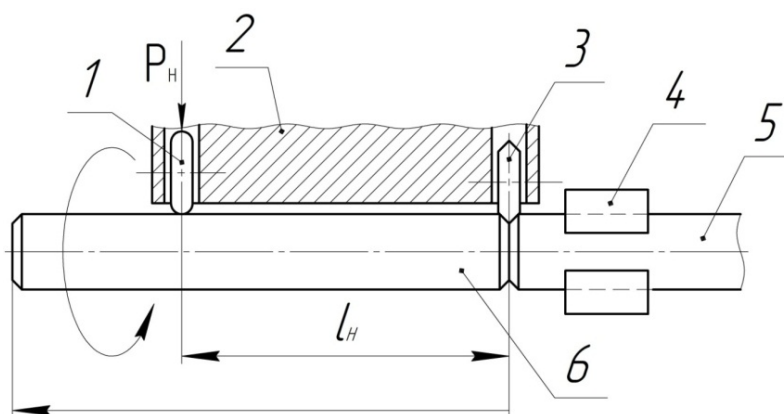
Схема разрезки прутка на длинномерные заготовки: 1 – нажимной ролик; 2 – ротор; 3 – клиновой инструмент; 4 – зажим; 5 – пруток; 6 – длинномерная заготовка
